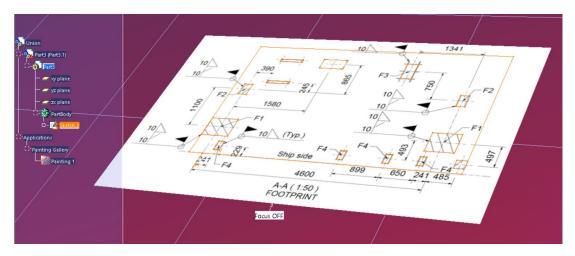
Proyección del plano base del pescante LH-60 de Viking. 2025. Sobre Catia v5. Fuente: 3D elaboración propia, plano: https://www.viking-life.com
